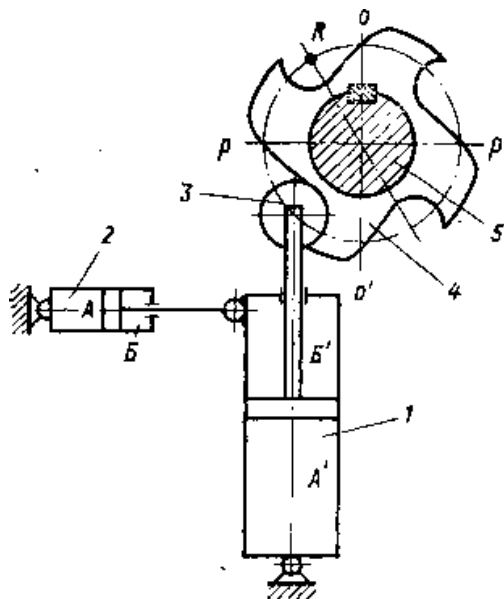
Схема механізму повороту ротора двома пневмоциліндрами:
